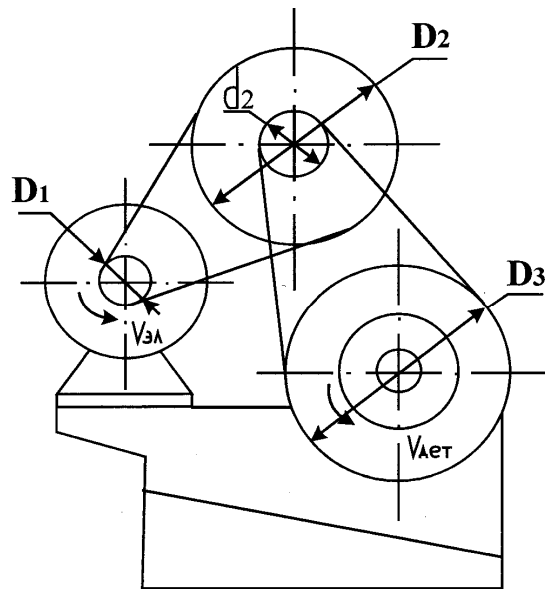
Схема привода вращения детали на круглошлифовальном станке
